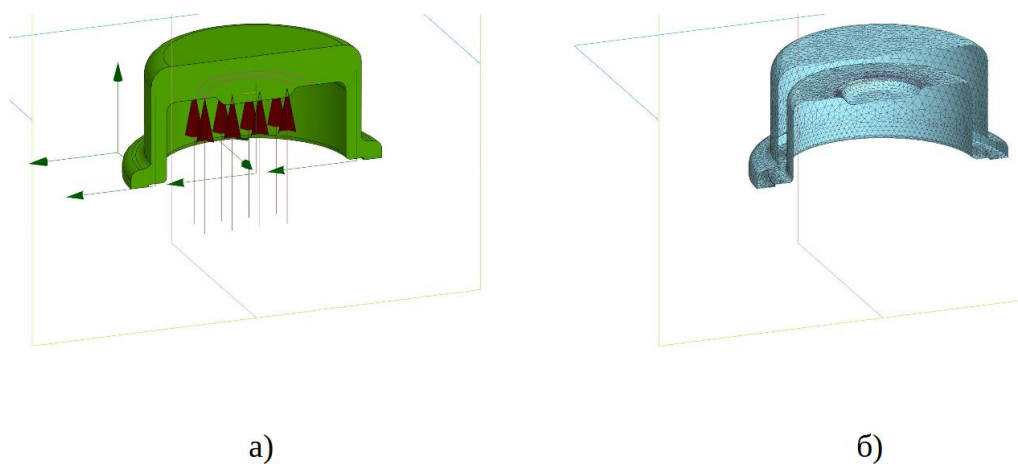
Крышка корпуса а) схема расстановки нагрузки и закрепления;
